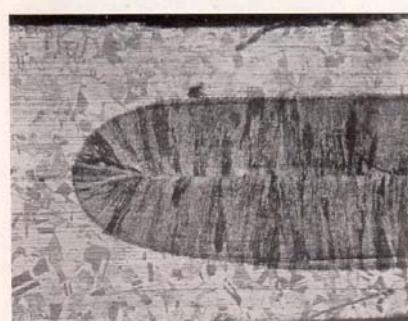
Nichtrostender Stahl-Punktschweißung Vergr. = 35 (39)
